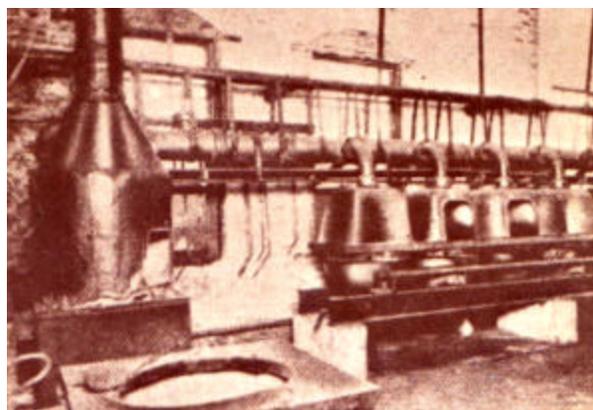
«El apartado», separación de oro y plata, en la planta de la fundidora 2 (AGENL).
